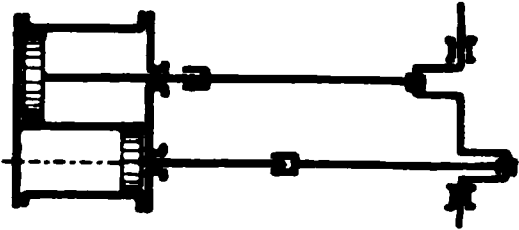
Woolfsche Maschine mit entgegengesetzt gerichtetem Kolbenlauf, Kurbeln unter 180° versetzt.
